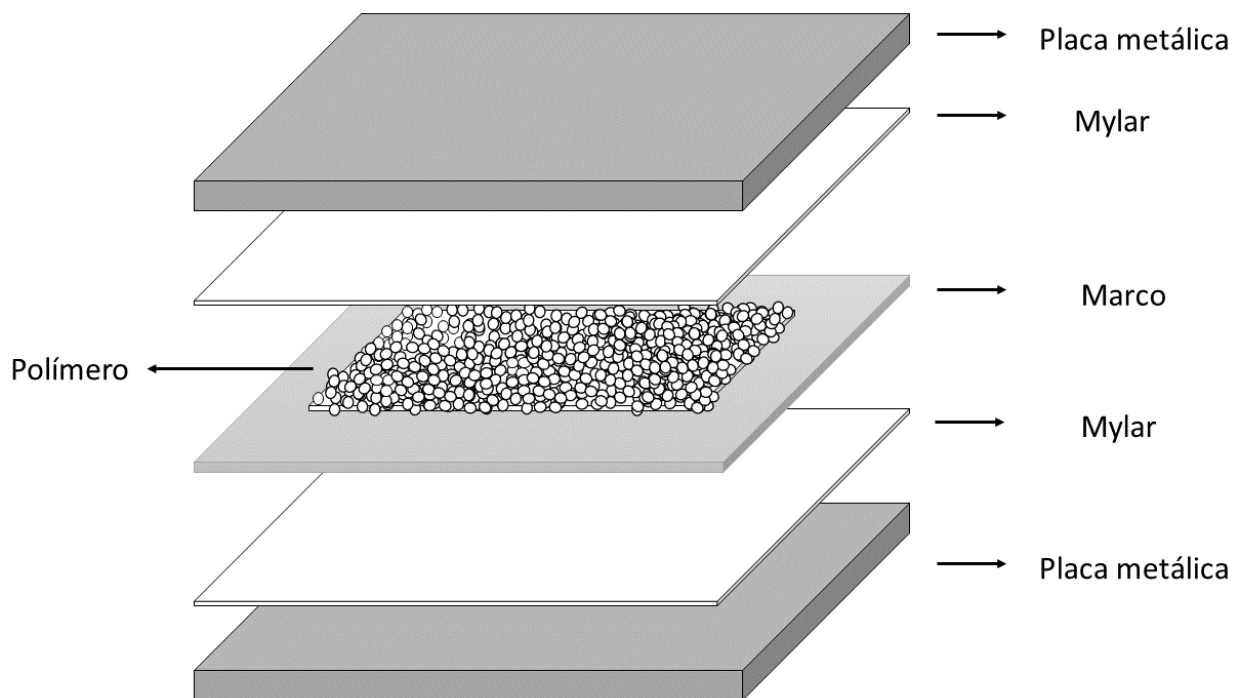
Esquema del molde previo a ser colocado en la prensa hidráulica.
